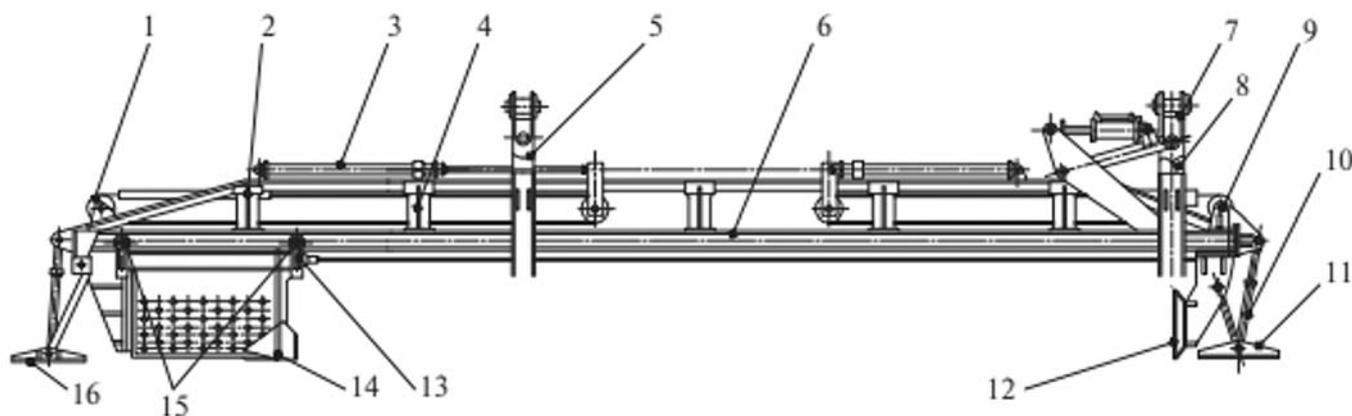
Рабочее оборудование с продольным по оси канала движением ковша: 1, 2, 9 - концевые блоки; 3, 7 - гидроцилиндры передвижения ковша; 4 - рама рабочего оборудования; 5, 8 - передний и задний телескопы стрелы; 6 - направляющие балки; 10 - винтовая штанга; 11 - передняя подвижная опора; 12 - упорный щит; 13 - траверса; 14 - рабочий орган (ковш); 15 - роликовые опоры траверсы; 16 - задняя подвижная опора
